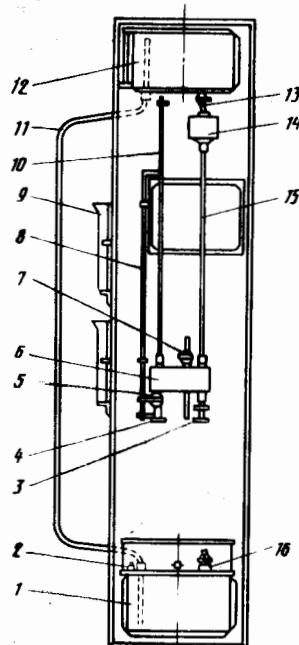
Схема прибора для проверки пропускной способности дозирующих элементов карбюратора:
